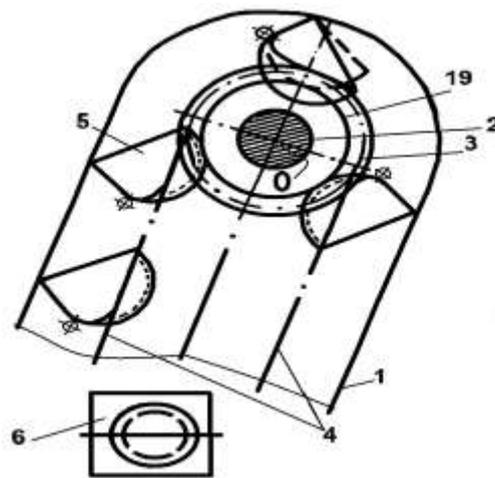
Наклонный ковшовый элеватор с ковшами ПФ
